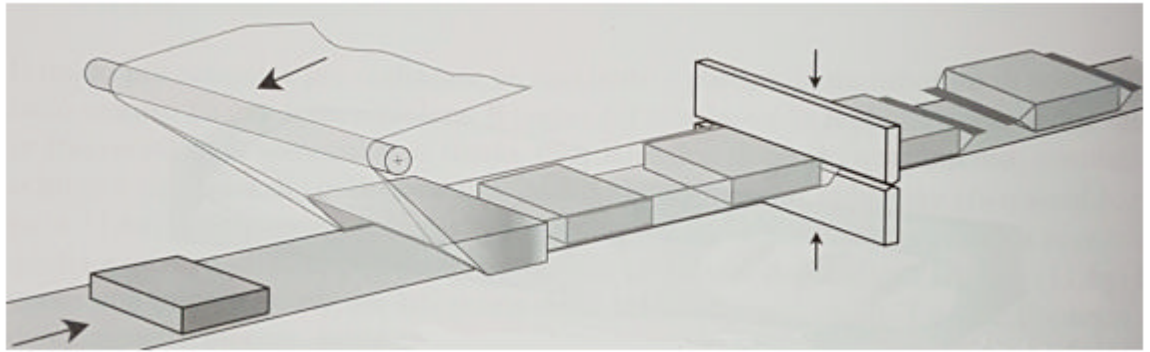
Схематичний вигляд поперечного зварювання в горизонтальній обгортковій машині.
